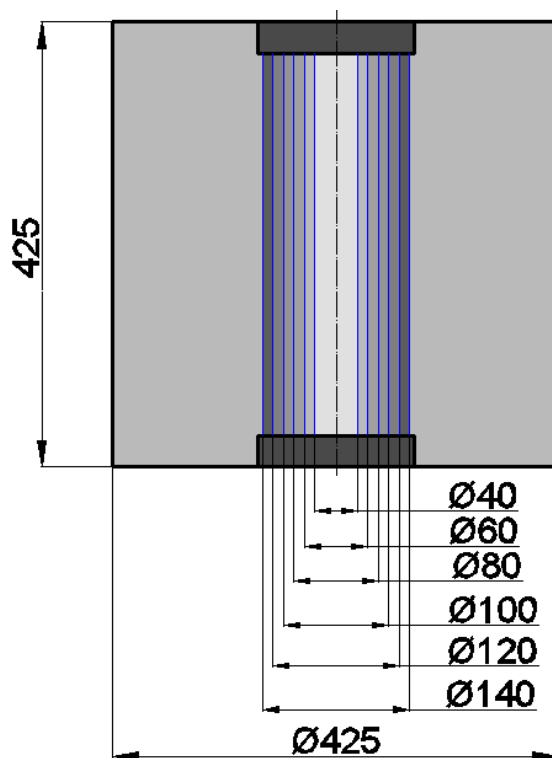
Исходная заготовка (из составных цилиндров)
